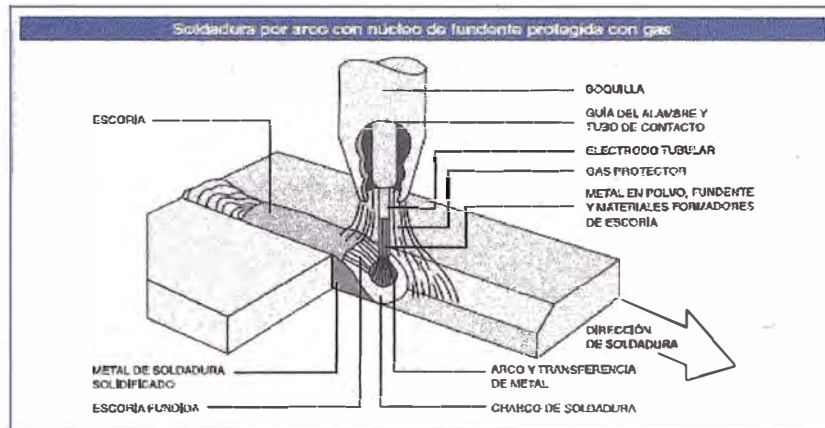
Esquema Proceso FCAW con gas (Fuente: Manual de Soldadura Indura)
